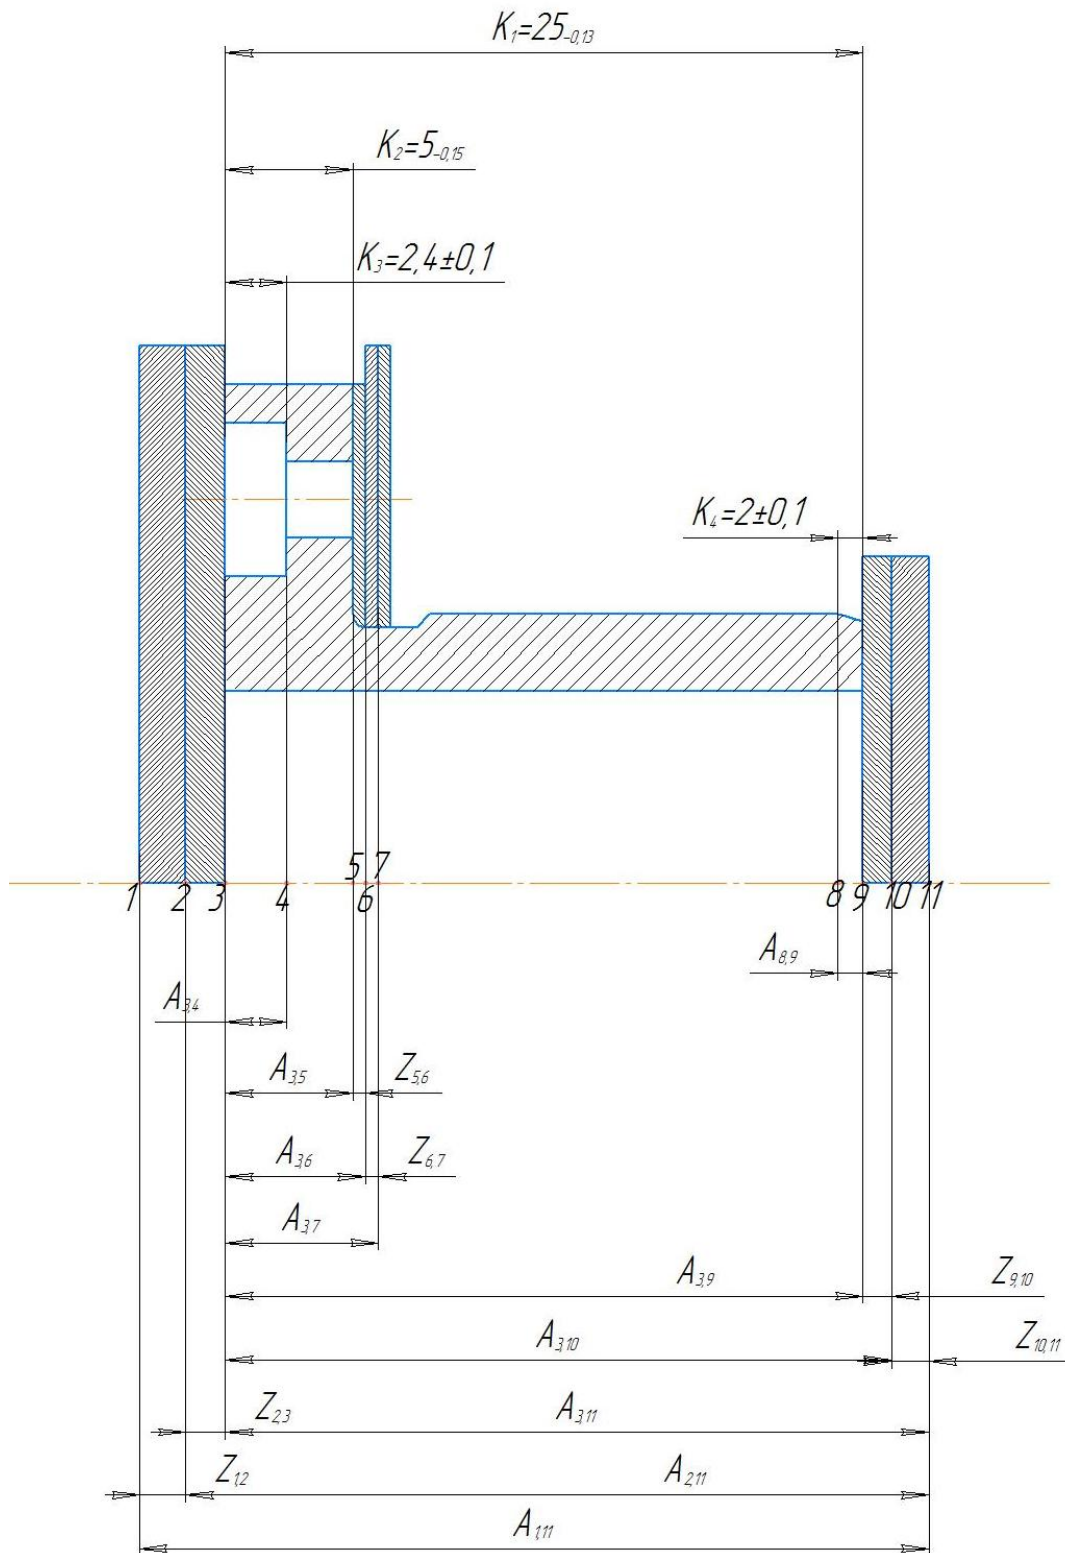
Размерная схема детали «Втулка подшипниковая» в продольном направлении
